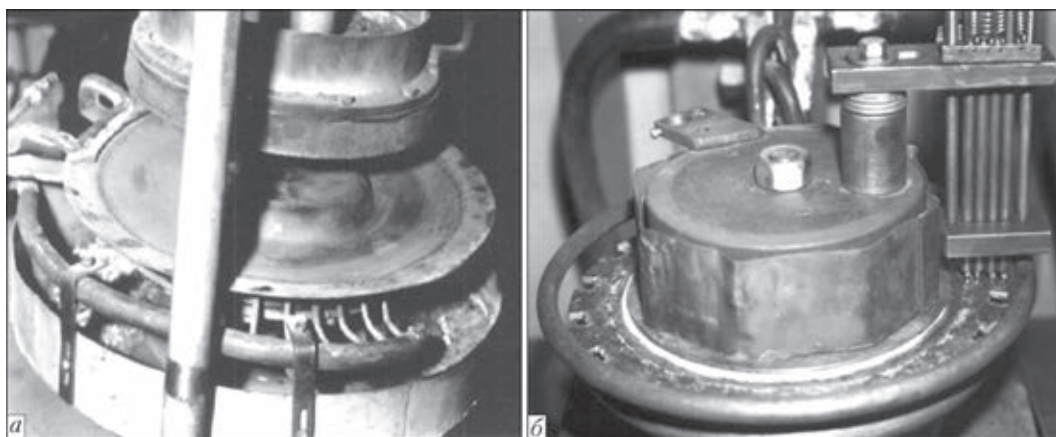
Устройства для наплавки цельноштампованного сплошного ножа с помощью сегментного индуктора (а) и ножей-ботворезов зубчатой формы в двухвитковом кольцевом индукторе (б) [3]
